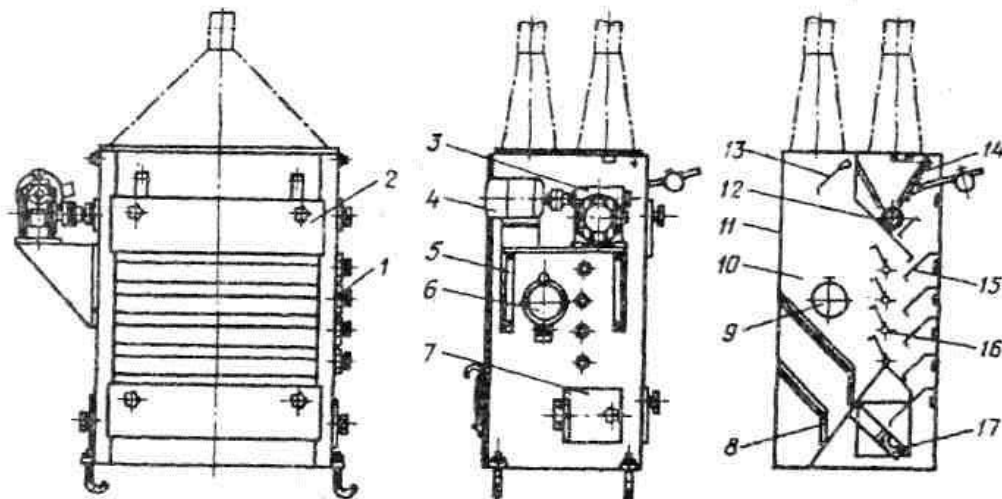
Аспирационная колонка А1-БКА: 1 — рукоятка; 2 — съемная фортка; 3 — редуктор; 4 — электродвигатель; 5 — кронштейн; 6, 7, 9 — смотровые окна с лючками; 8 — клапан; 10 — осадочная камера; 11 — корпус; 12 — питающий валик; 13, 16 — поворотные клапаны; 14 — грузовой клапан; 15 — неподвижный скат; 17 — устройство для выделения металломагнитных примесей
